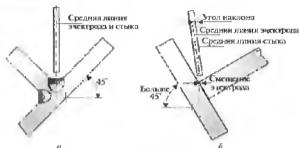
Сварка тавровых соединений «в лодочку»
